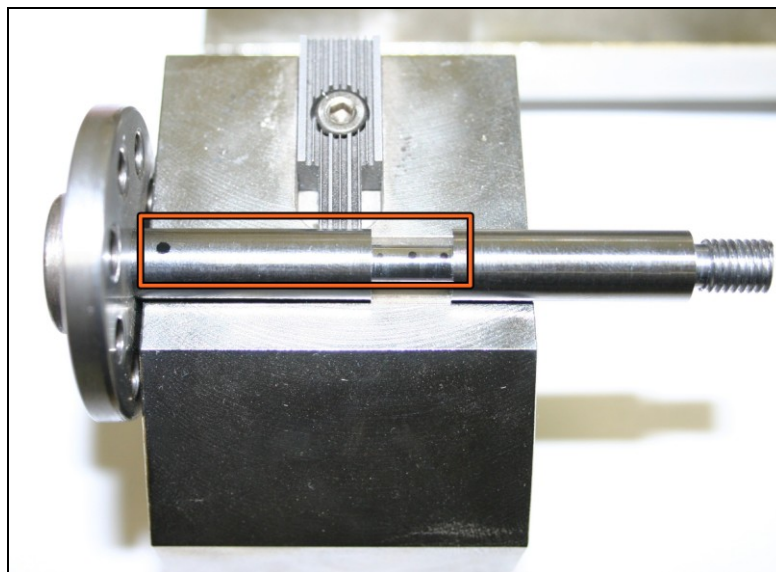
Probe mit Markierungen für das Anschweißen der Thermoelemente
